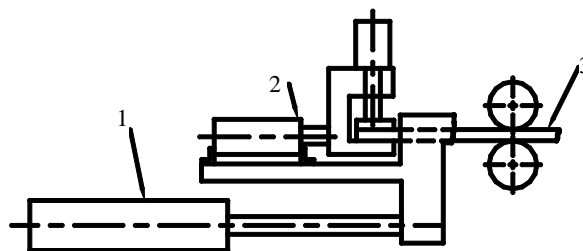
Схема устройства, использующего механизм, который поглощает разницу между скоростью заготовки в выходе и скоростью втягивающего цилиндра
